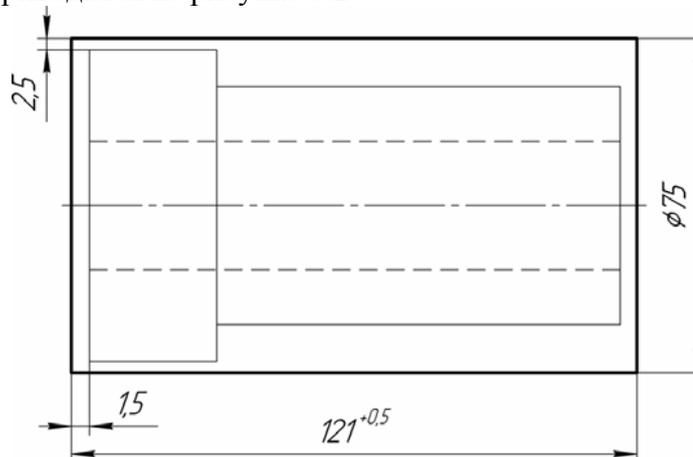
Эскиз заготовки для втулки ТЭТО-КП.543.08.01.006
